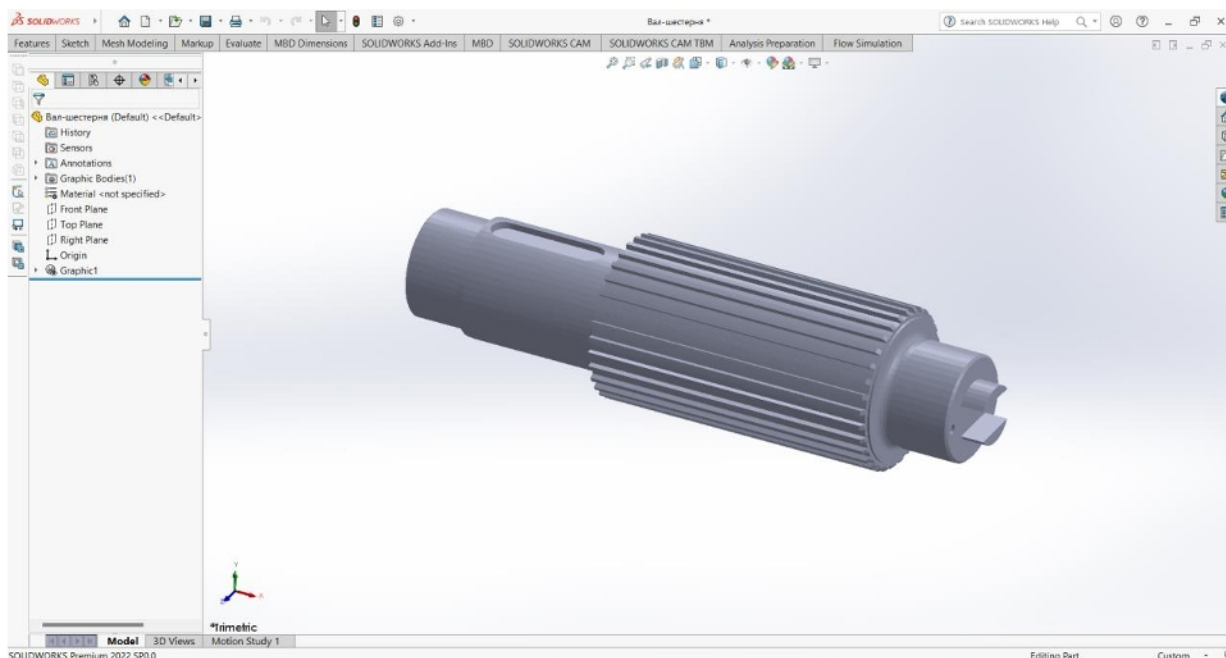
3D модель «Вал-шестерні» зроблена в SolidWorks
